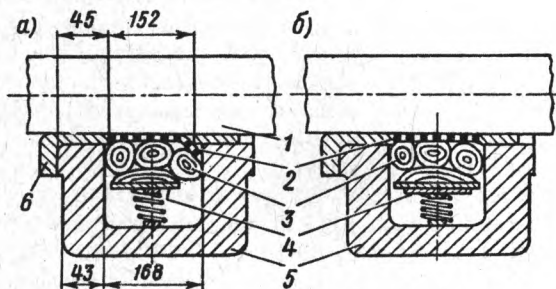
Серийный (а) и модернизированный (б) моторно-осевой подшипник тепловоза ТЭЗ: 1—ось; 2—войлок; 3—пряжа; 4—планка; 5—крышка; 6—подшипник
